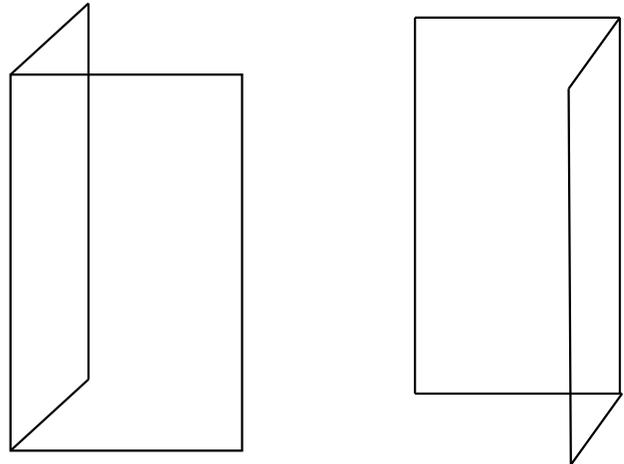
Armado por separado de las dos estructuras de la caja para hacer el molde.
